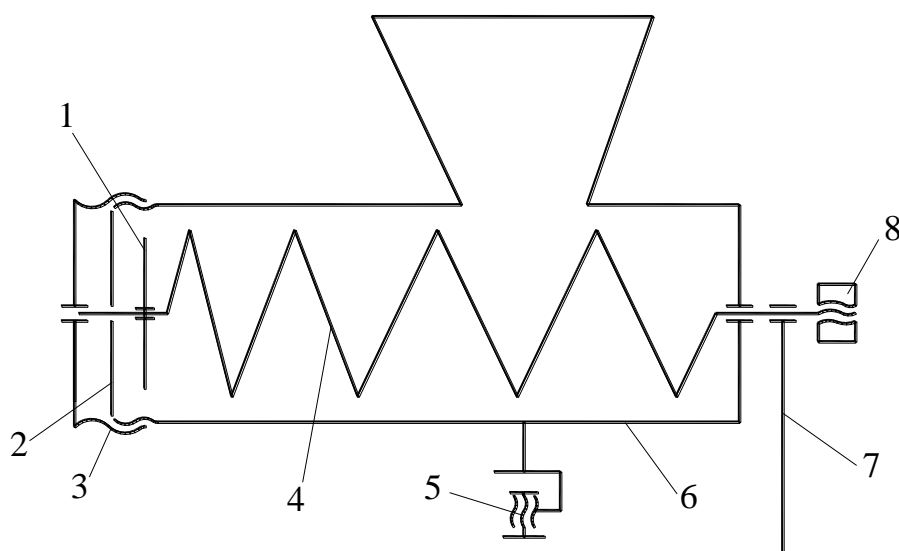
Структурна схема побутової шнекової м'ясорубки: 1 – ніж; 2 – решітка; 3 – гайка; 4 – шнек (валик, витки); 5 – гвинт; 6 – корпус (корпус, втулка, прокладка); 7 – ручка; 8 – гайка.
